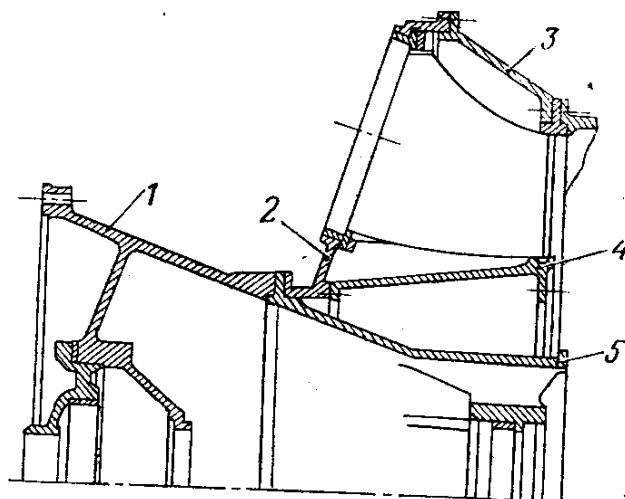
Корпуса заднего подшипника и заднего газосборника:
